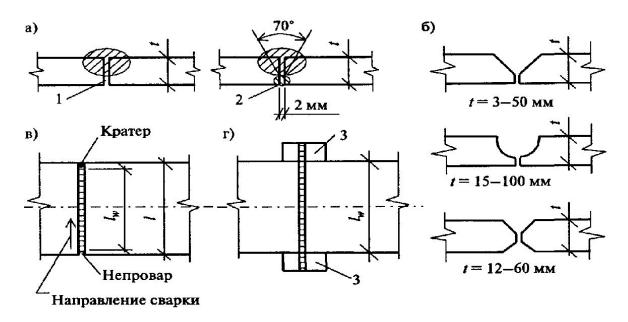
Выполнение сварных соединений: а) подварка корня шва; б) разделка кромок соответственно: V-образная, U-образная, X-образная; в) образование непровара и кратера по длине шва; г) выполнение шва на технологических подкладках; 1 — непровар корня шва; 2 — подварка корня шва; 3 — технологические подкладки
